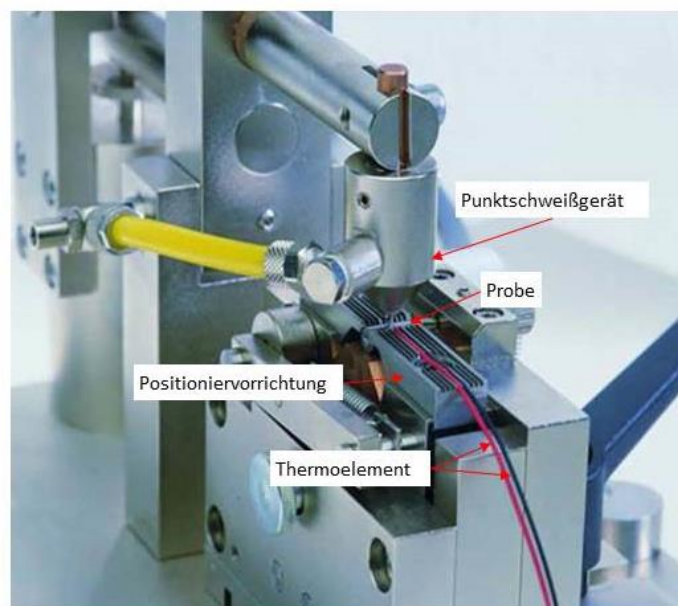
Punktschweißgerät mit Positioniervorrichtung.
